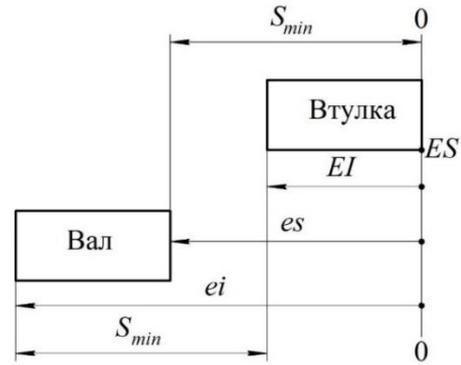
Схема расположения полей допусков при цифровом подборе
